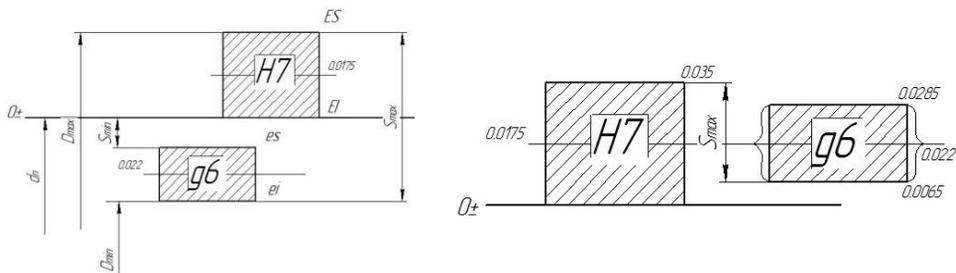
Схема расположения полей допусков двухосных соединений «вал-отверстие» в системе отверстия
